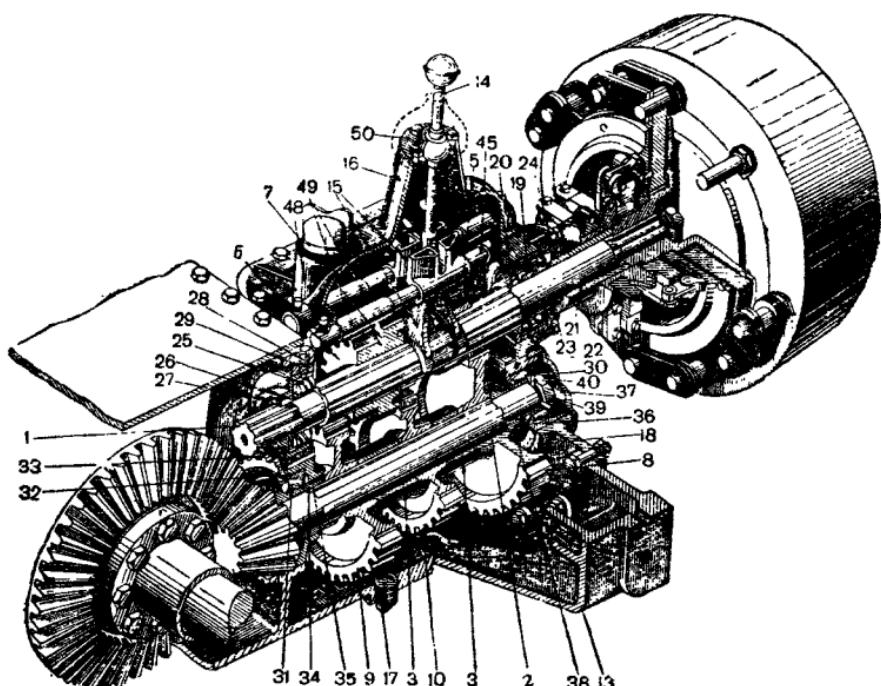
Общий вид коробки передач трактора ЧТЗ.
